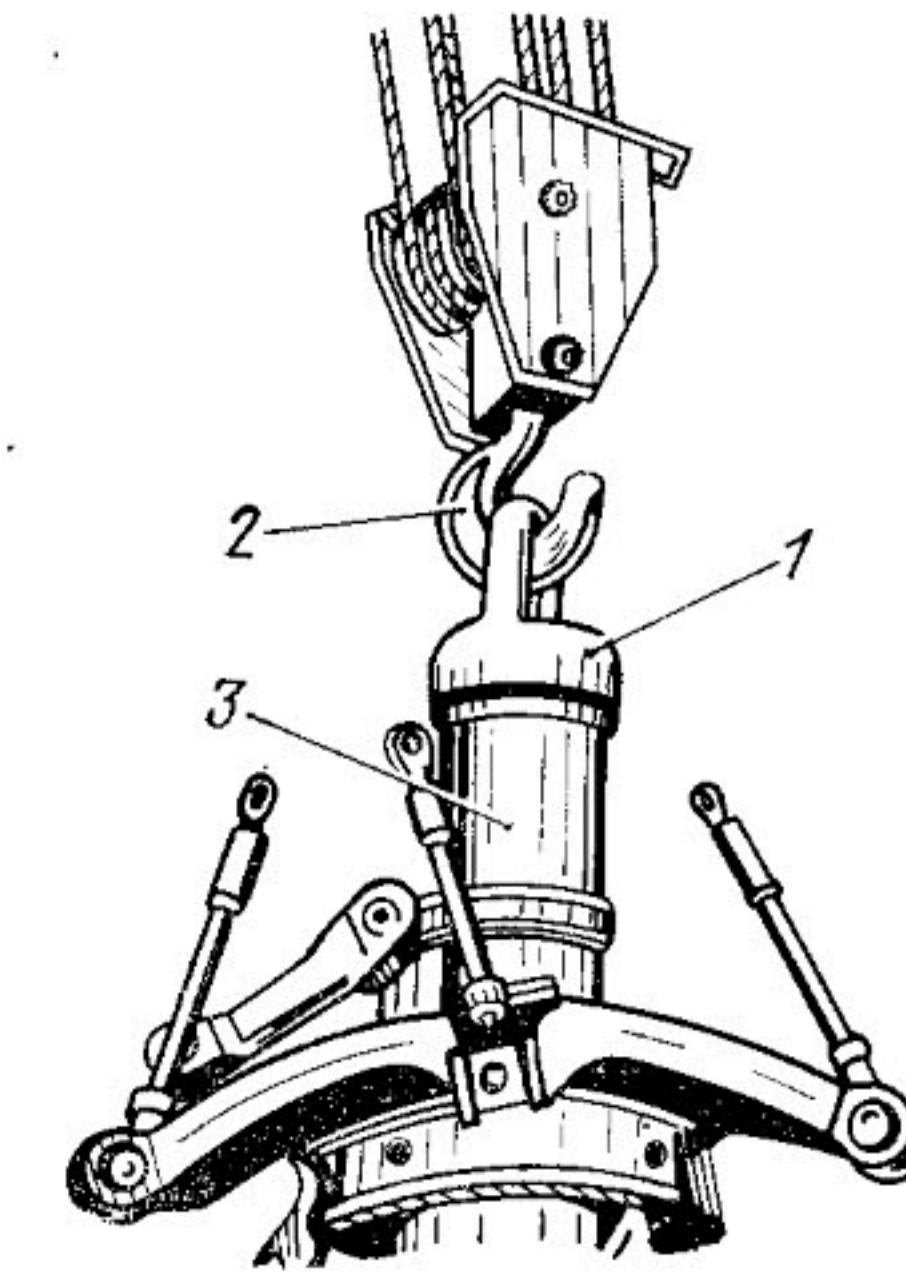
Приспособление (рым-гайка) для монтажа главного редуктора Р-7:
